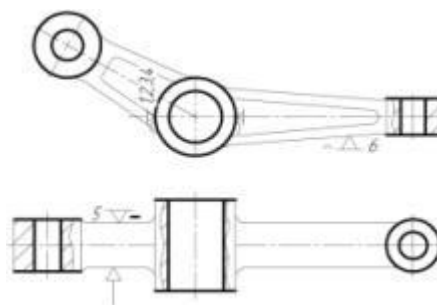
Схема базування заготовки на комплексній із ЧПК операції
